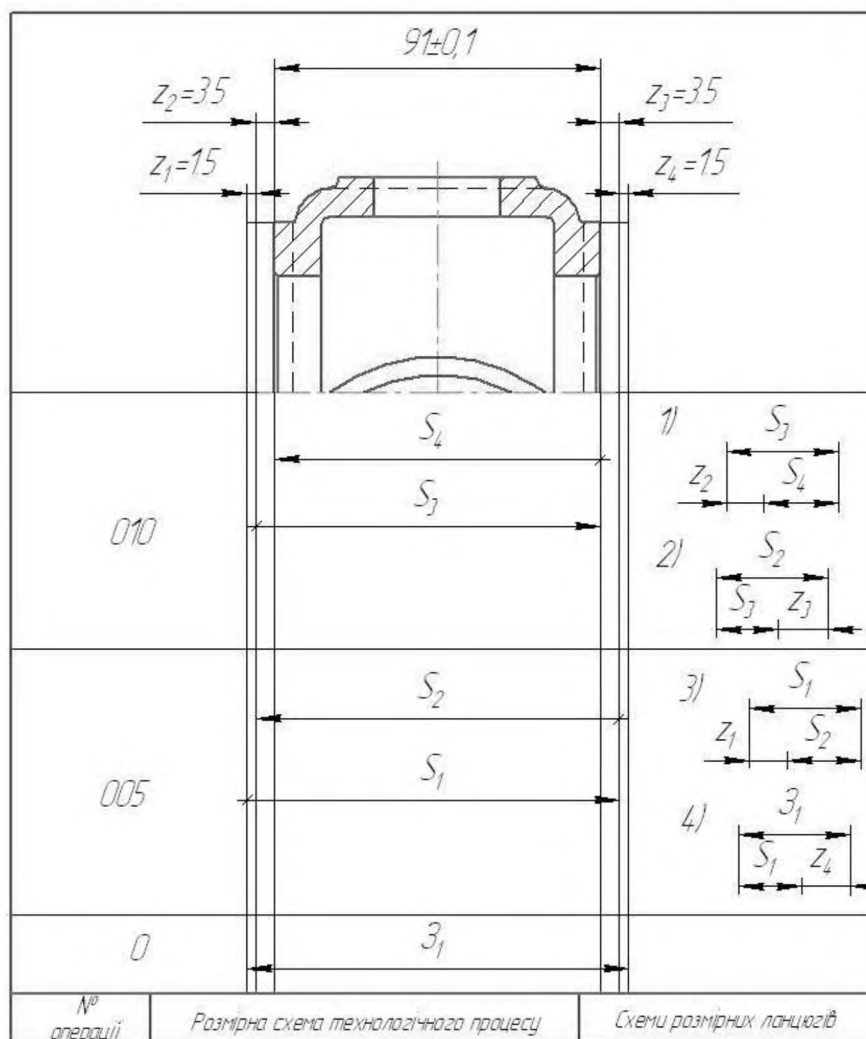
Побудова розмірної схеми технологічного процесу обробки деталі
